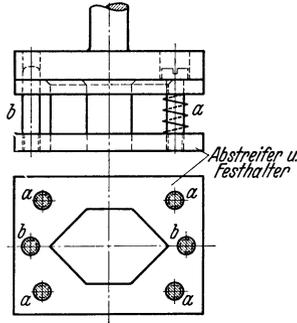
Federnder und geführter Abstreifer und Festhalter. a Aufhängeschrauben. b Führungsbolzen.
